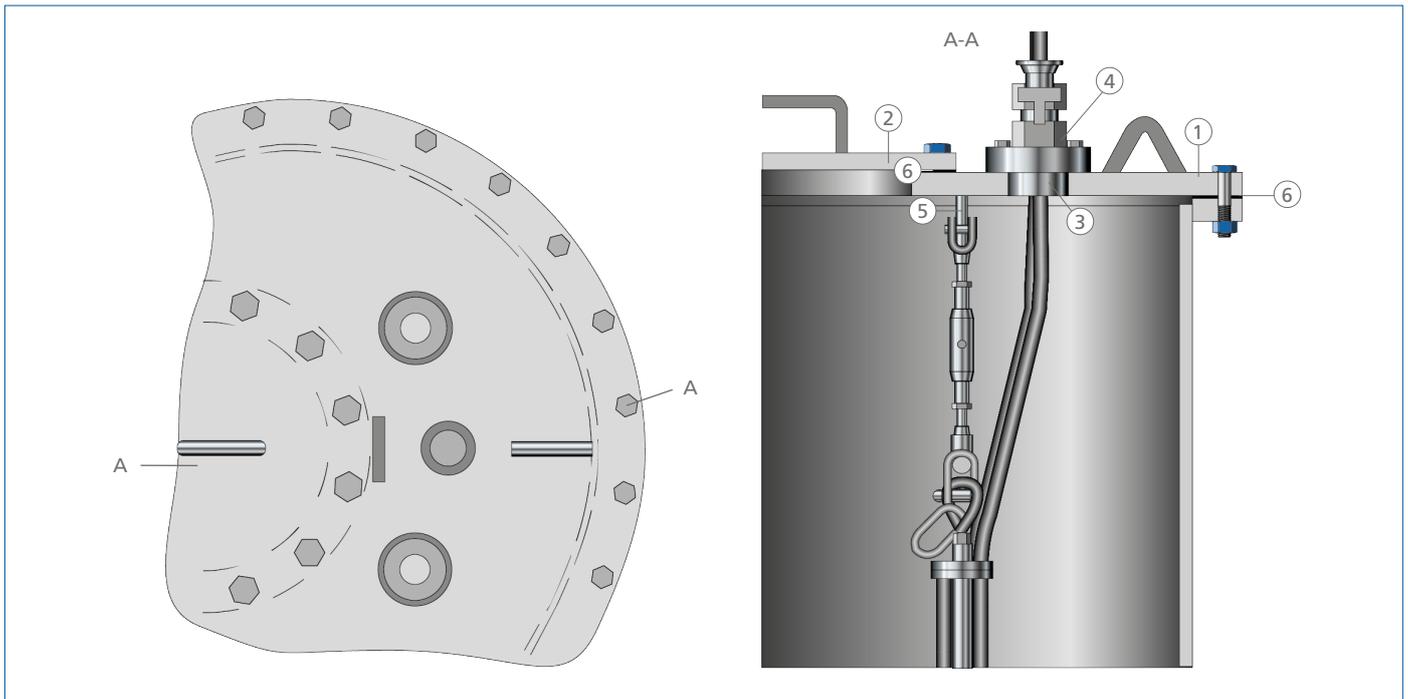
Die Ausführung mit Einschweißhülse ist die von KSB empfohlene Variante.
